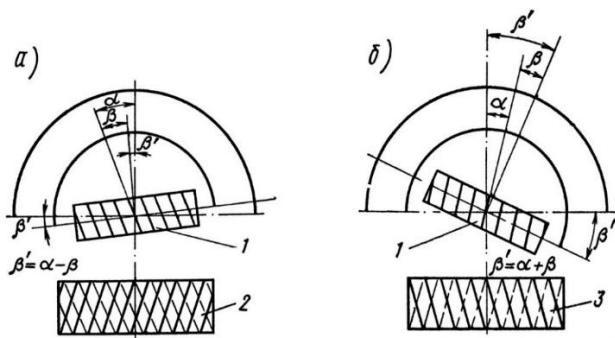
Установлення кута нахилу фрези під час нарізання циліндричних зубчастих коліс із косими зубцями: 1 – черв'ячна фреза з правим нахилом гвинтової лінії; 2 – зубчасте колесо з правим нахилом зубців; 3 – зубчасте колесо з лівим нахилом зубців
